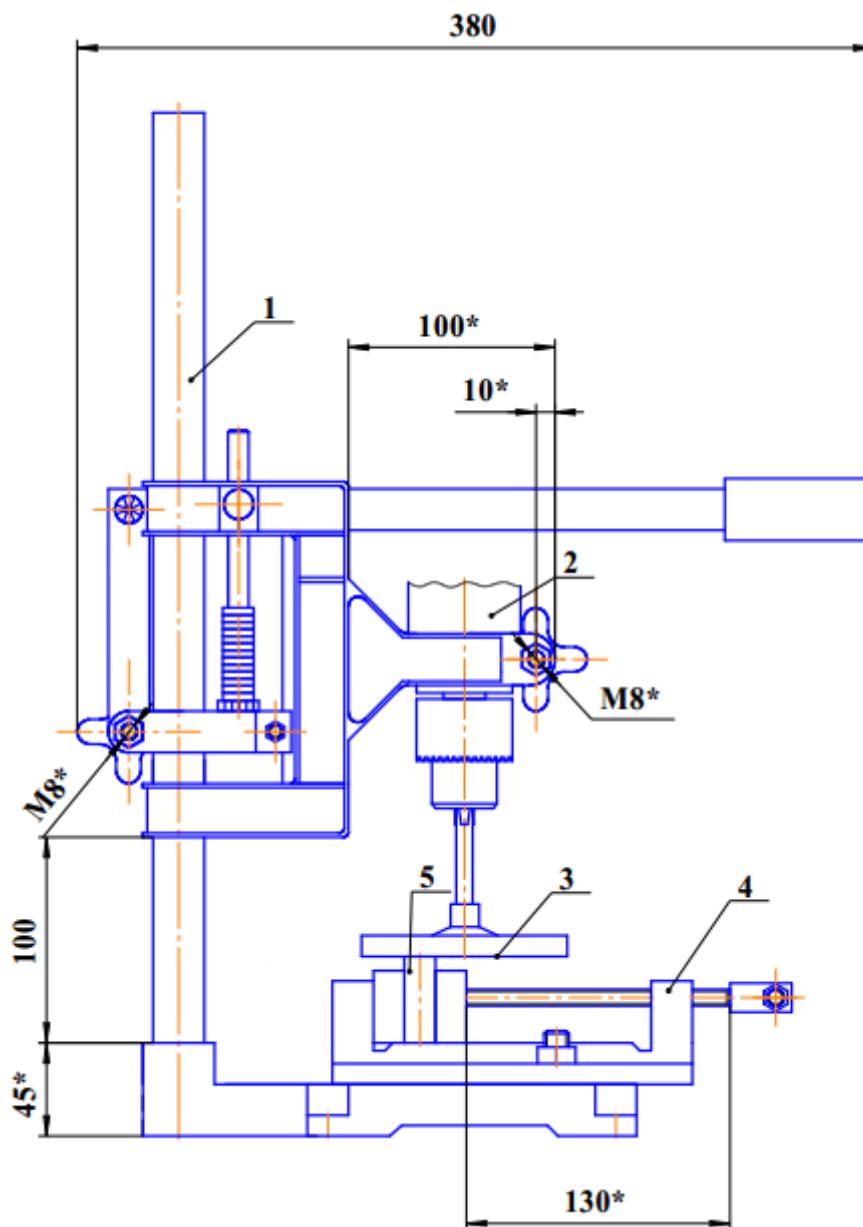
Установка для испытания износостойкости наплавленных образцов [100]
